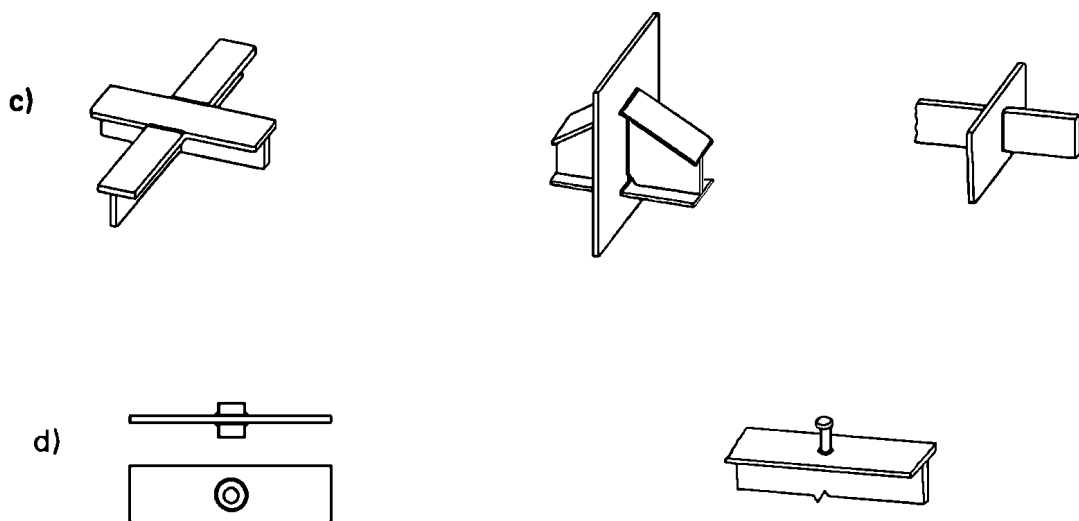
Esquemas de juntas soldadas e fundidas.
